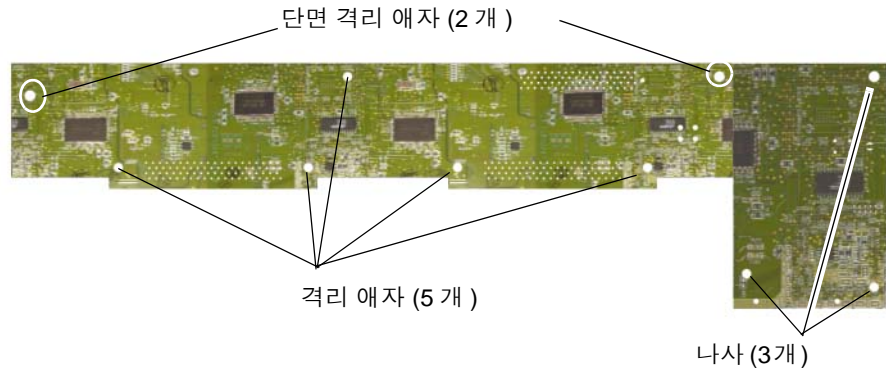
하위 인터페이스 보드 격리 애자 및 나사 위치
